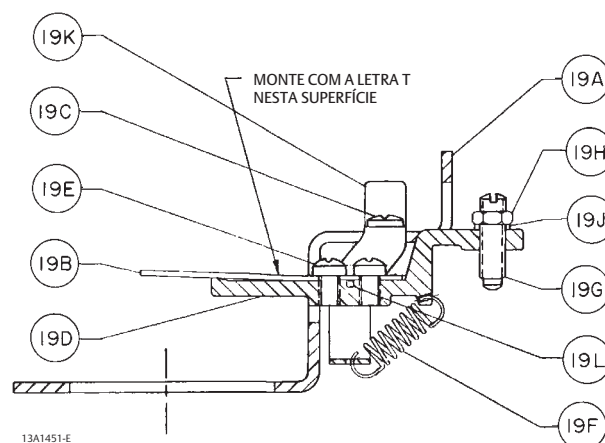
Desenho do Conjunto dos Posicionadores e Transmissores 3582 e 3583
